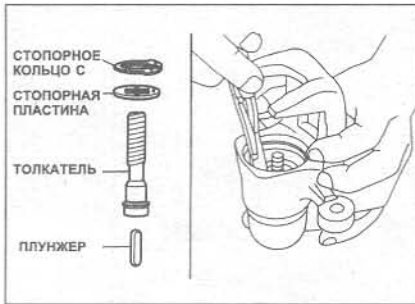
Установка стопорной пластины и деталей штанги толкателя в корпус суппорта (Глава 25)
